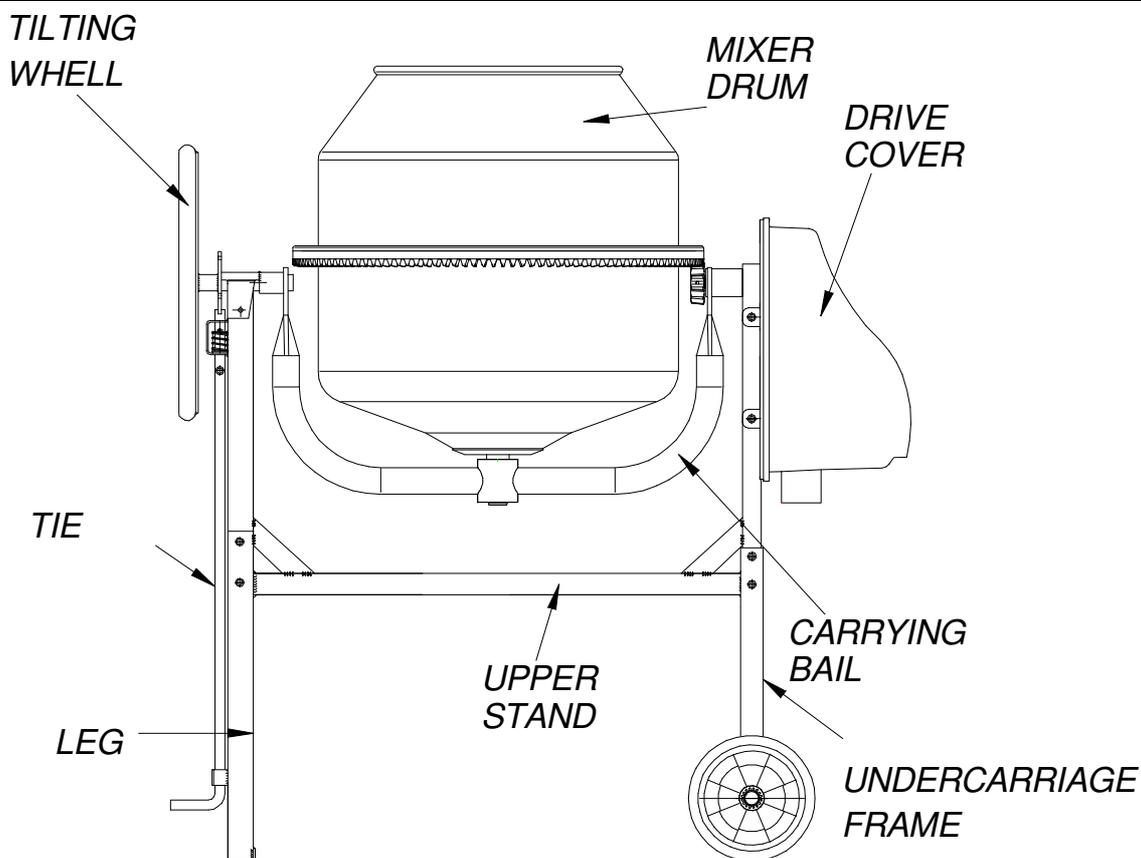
Bétonnière – vue d'ensemble [cuve, boîtier, étrier, châssis, trépied, pied, blocage, volant]
